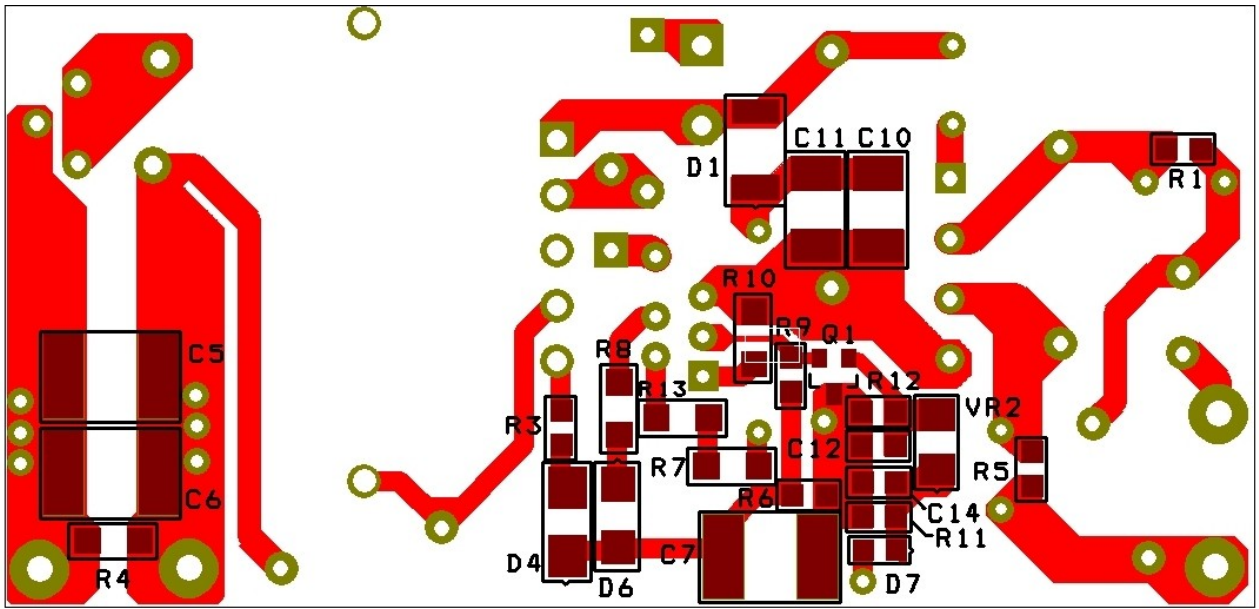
PCB DER-284 보드 레이아웃, Bottom 면
